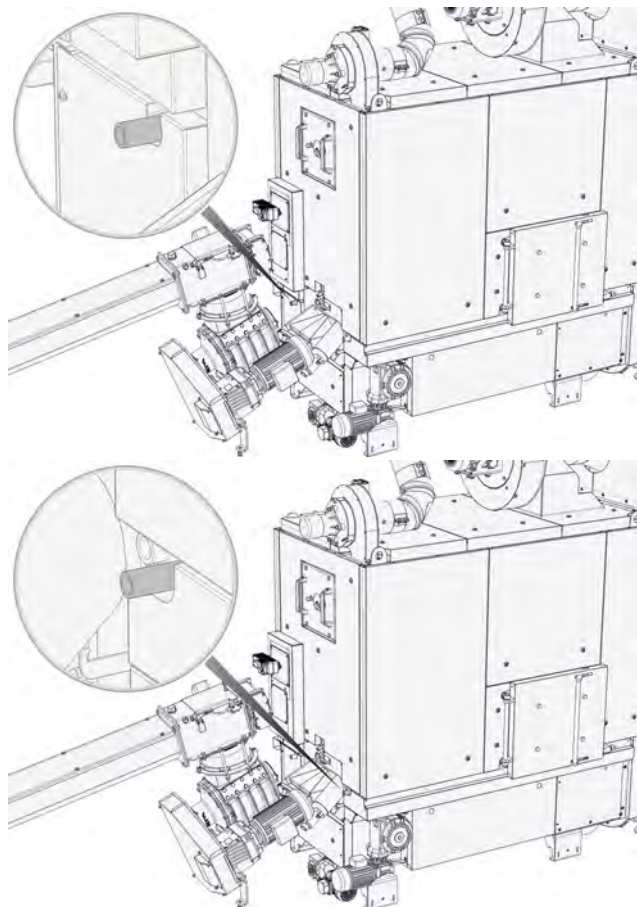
Raccords pour soupape thermique de la chambre de combustion
